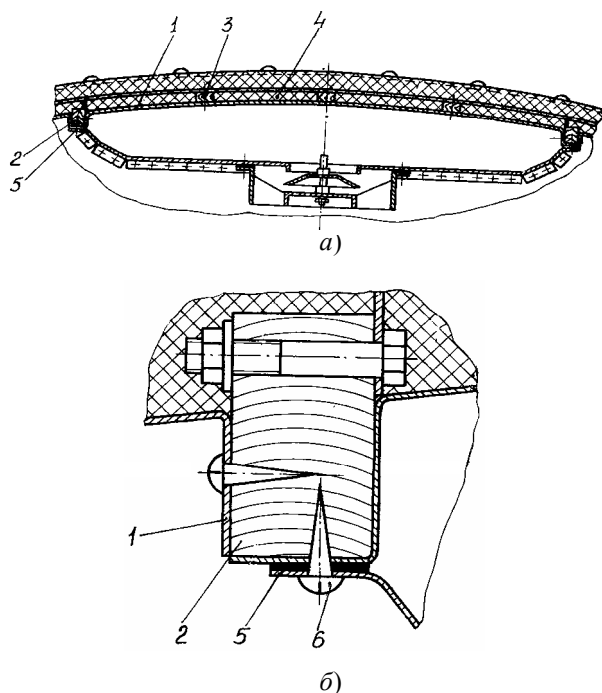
Поперечный разрез на вагоне модели 61-779: а – приточного воздуховода; б – узла крепления
